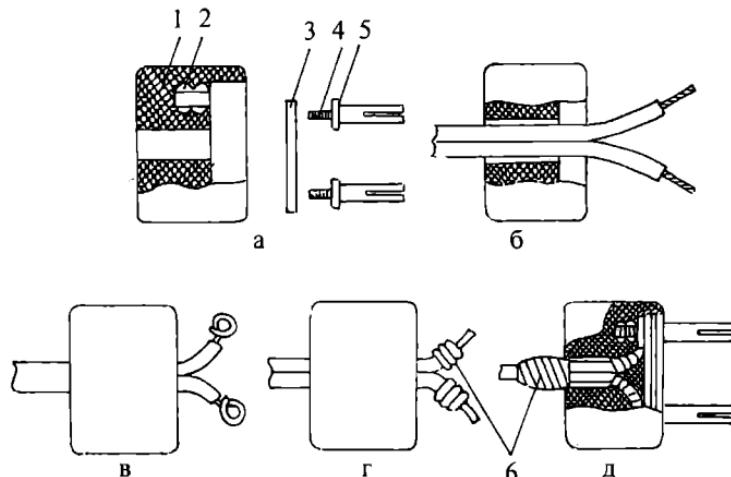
Монтаж и ремонт вилки с разрезными штифтами и цельным пластмассовым корпусом: а — разборка вилки; б — протягивание проводников и зачистка жил по длине 10–15 мм; в — загиб концов жил в петли; г — изоляция места закручивания жилы, образующей петлю; д — наложение на петли планки и закручивание штифтов в спецгайки; 1 — корпус; 2 — спецгайка; 3 — планка; 4 — разрезной штифт; 5 — гайка шестигранная; 6 — изоляционная лента
